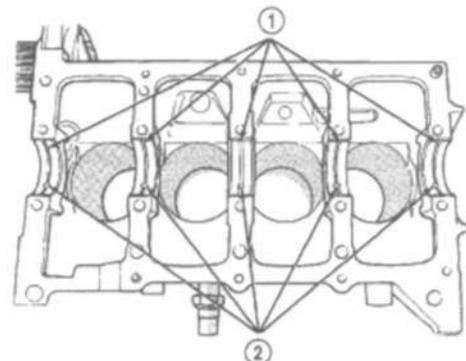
Установка верхнего вкладыша коренного подшипника 1 – СМАЗОЧНЫЕ КАНАВКИ. 2 – МАСЛЯНЫЕ ОТВЕРСТИЯ
